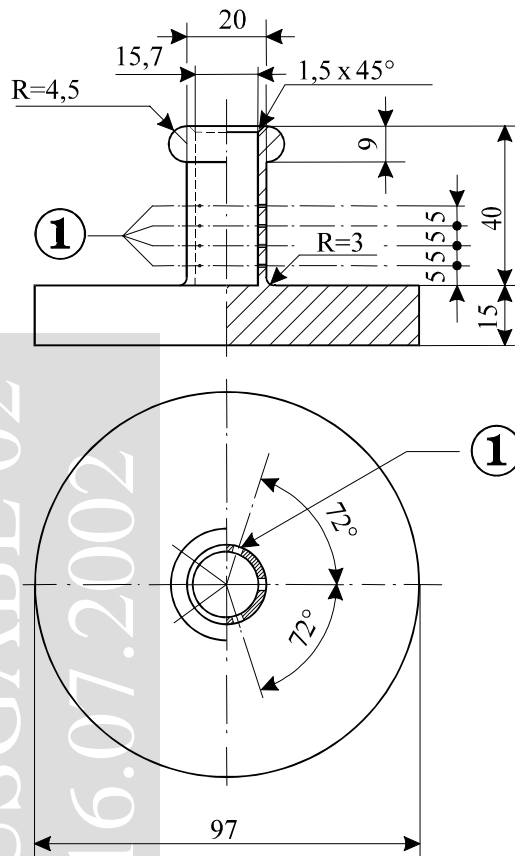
Hohler Bronzeyylinder, einseitig verschlossen
